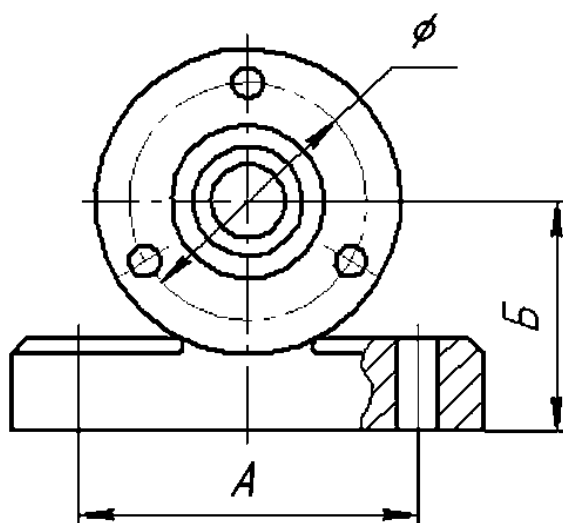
Образец выполнения присоединительных и установочных размеров.
